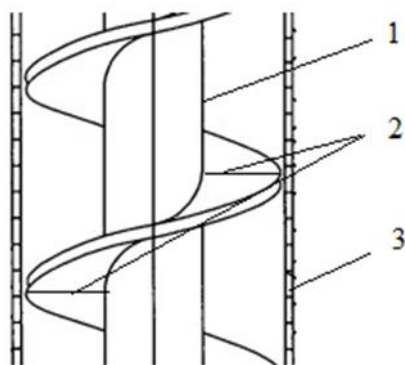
Принципиальная схема шнекового ворошителя: 1 – центральный цилиндрический полый корпус; 2 – витки шнека с прямолинейной образующей; 3 – отверстия в корпусе для вентилирования
